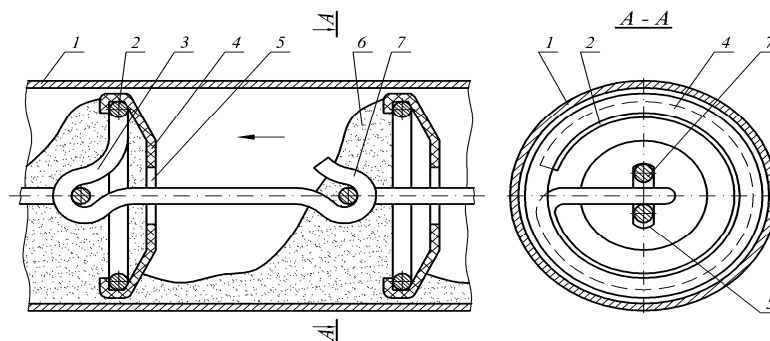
Конструктивна схема робочого органу шайбового конвеєра
